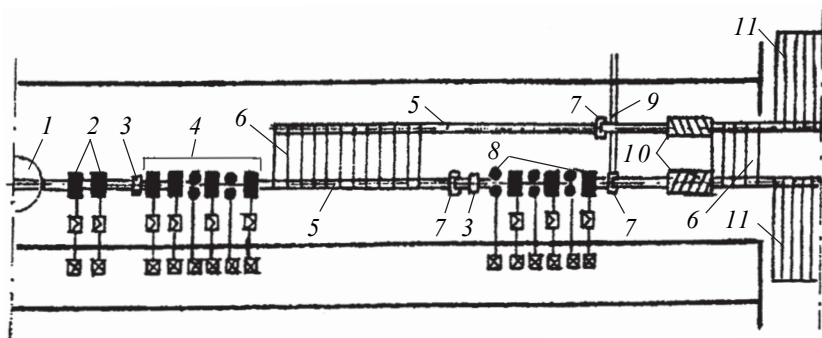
Схема расположения оборудования заготовочного стана<sup>4</sup>:
